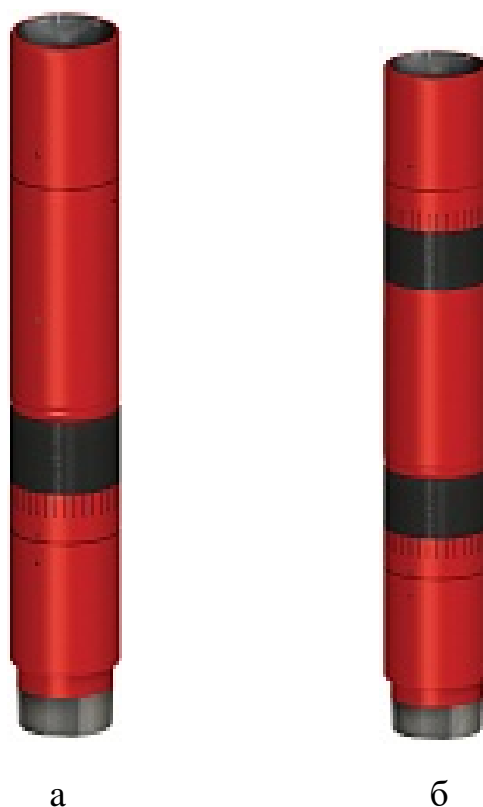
Пакеры за колонный гидромеханический проходной: а – типовой, б – двойного типа
